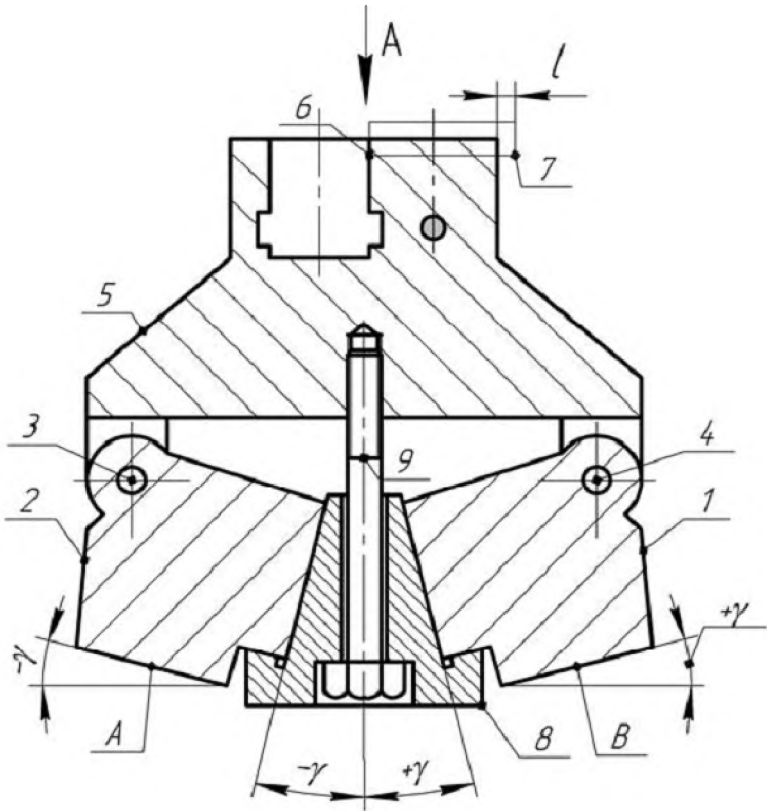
Главный вид многоместного кассетного приспособления
